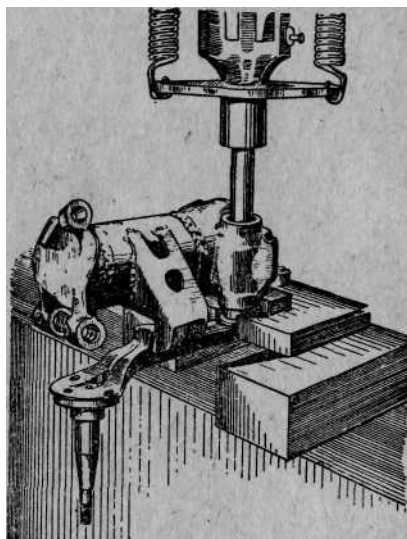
Оправка для выпрессовки и запрессовки втулок шкворня.
